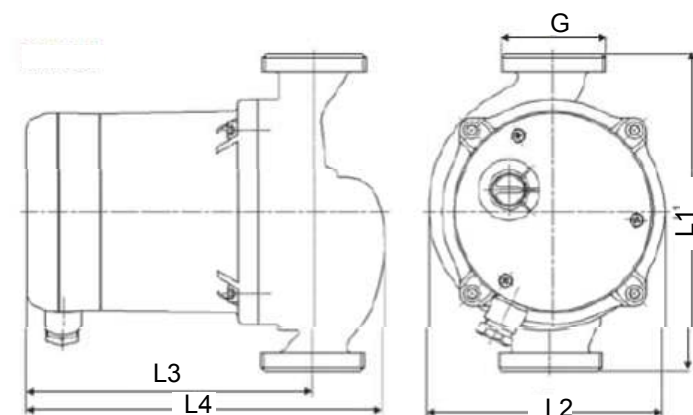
Габаритные размеры Calio-Therm NC 25-70
